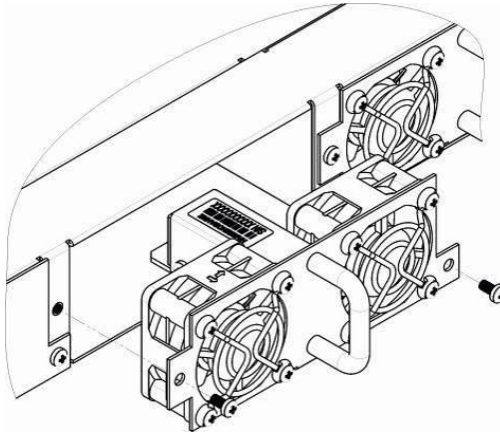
Блок вентиляции SMG-2016. Крепление в корпус
